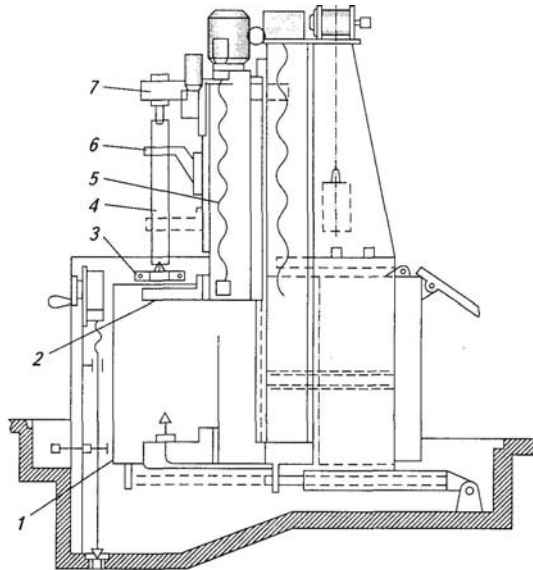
Схема універсального агрегатного верстата для гартування деталей типу тіл обертання після індукційного нагрівання
